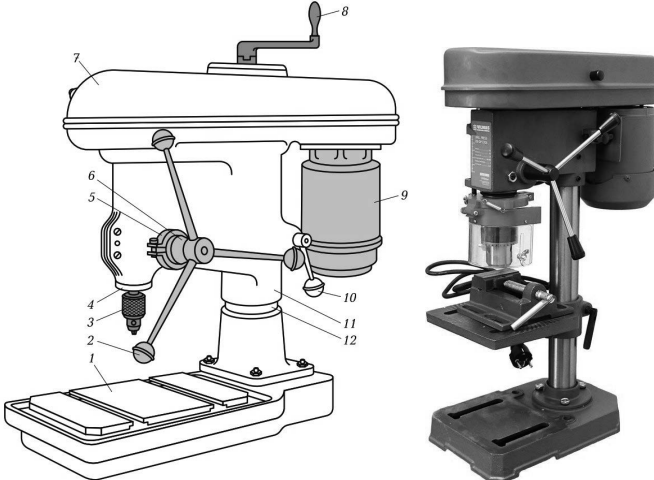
Настільний свердлильний верстат: 1 – стіл; 2, 8, 10 – рукоятки; 3 – трикулачковий патрон; 4 – шпиндель; 5 – хомутик; 6 – лімб; 7 – кожух; 9 – електричний двигун; 11 – корпус; 12 – колона
